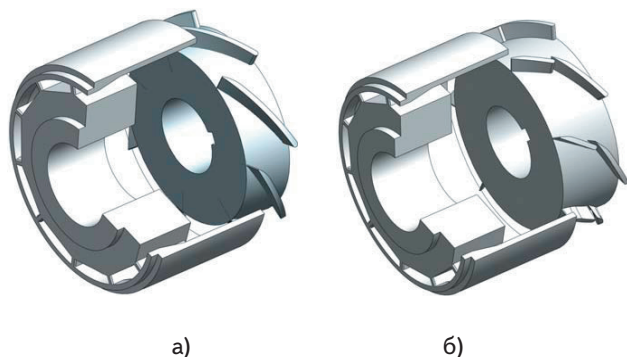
Малогабаритна ступень шнекового типу: а) робоче колесо зі звичайними лопатями; б) робоче колесо з біпланними лопатями
